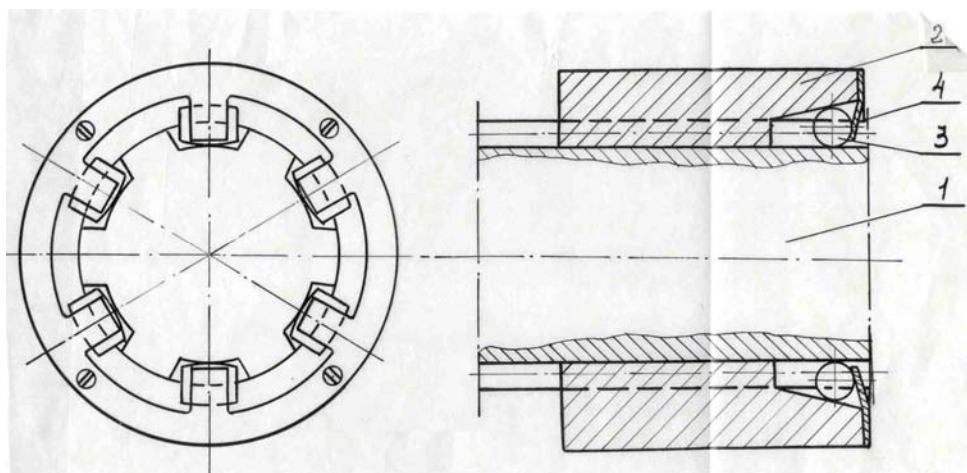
Механізм одностороннього гальмування в шліцевій передачі вал – колесо
